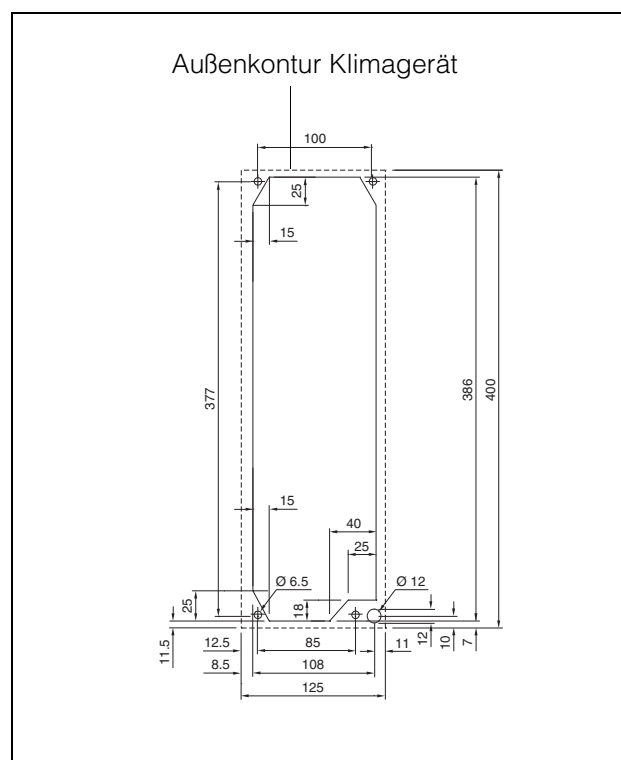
Montageausschnitt und Bohrungsmaße bei Geräteeinbau (Kompletteinbau)
